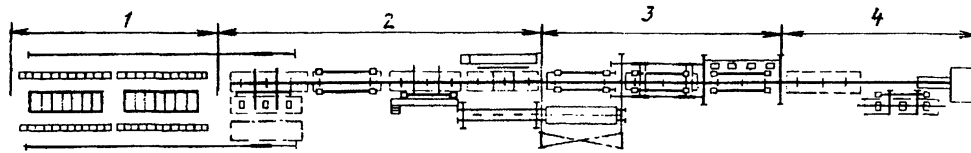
Принципиальная технологическая схема поточной линии сборки и сварки оснований платформ полурипов
